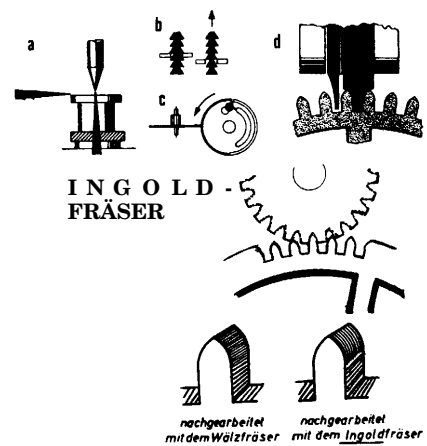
Wälzmaschine zur Zahnrad-Verbesserung; Ingold-Fräser zum Vergleich
